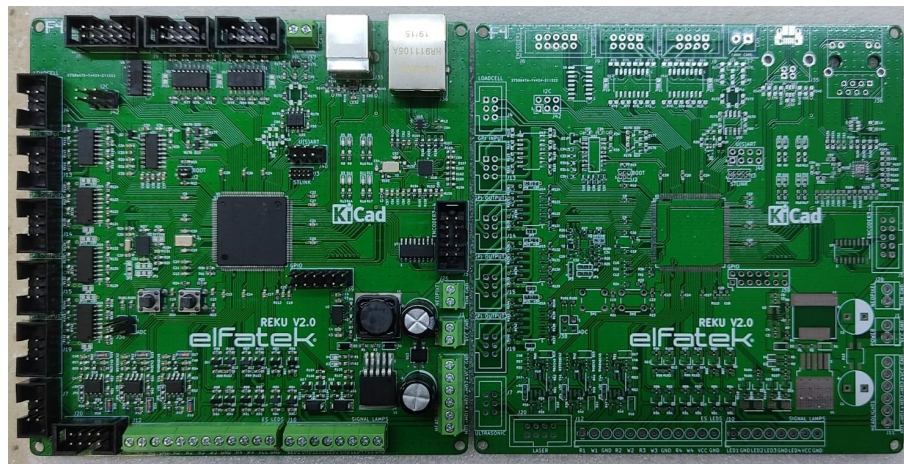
PCB Tasarımın 3 Boyutlu Montajlı Gösterimi
